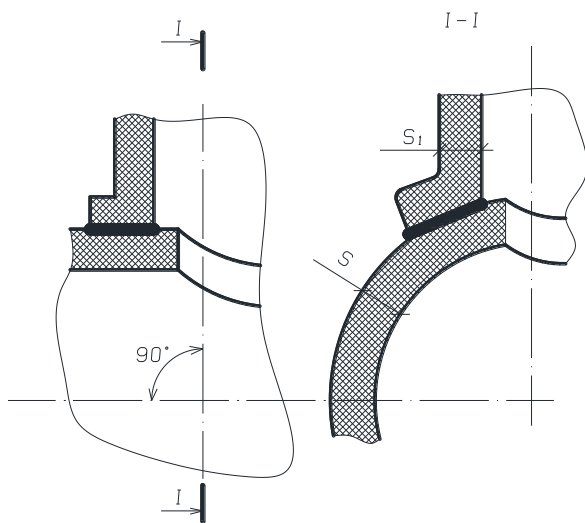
Конструктивные элементы шва сварного соединения (шов Т4)
